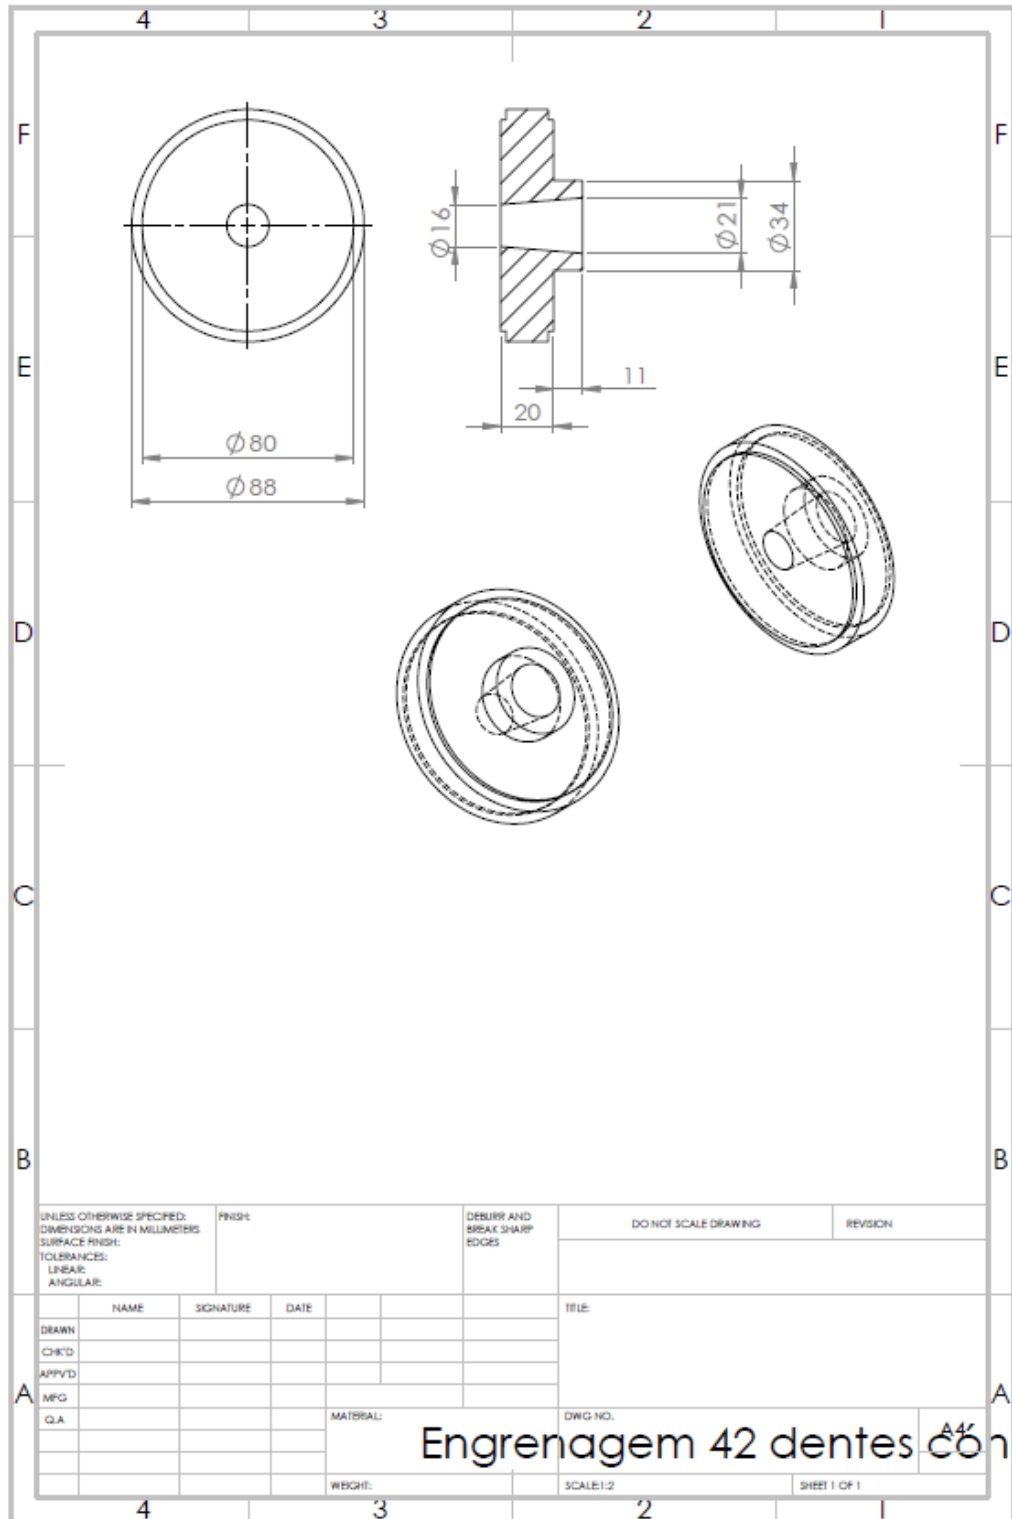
C, Desenho para engrenagem de 42 dentes com um perfil interior cônico [Foto do autor].
